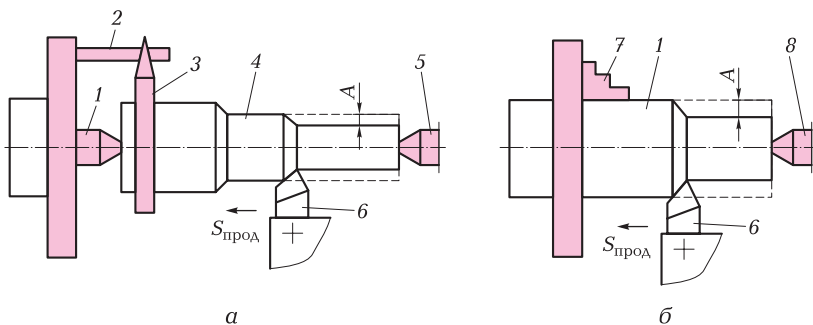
Схемы установки заготовки на токарном станке: а — в центрах; б — в самоцентрирующем патроне
